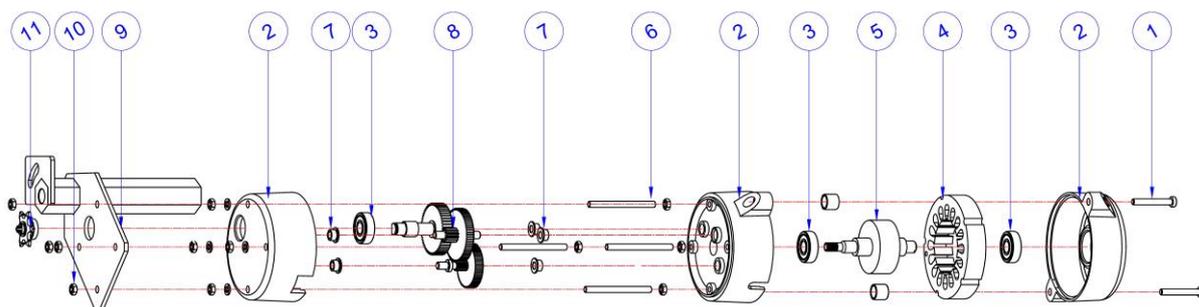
Peças do motor do comutador CM-1, CM-1M, CM-2 ou CM-2M.
